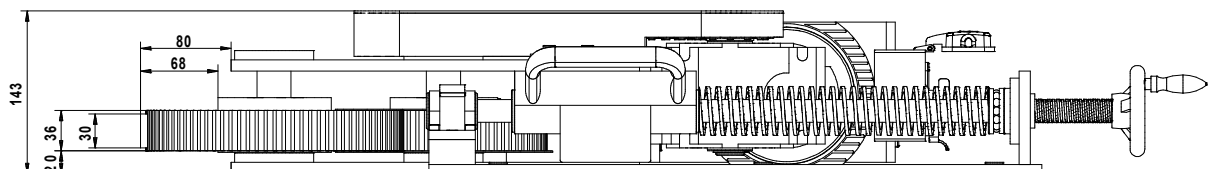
Seitansicht, Einbauhöhe Riementrieb in unterster Einbauhöhe
